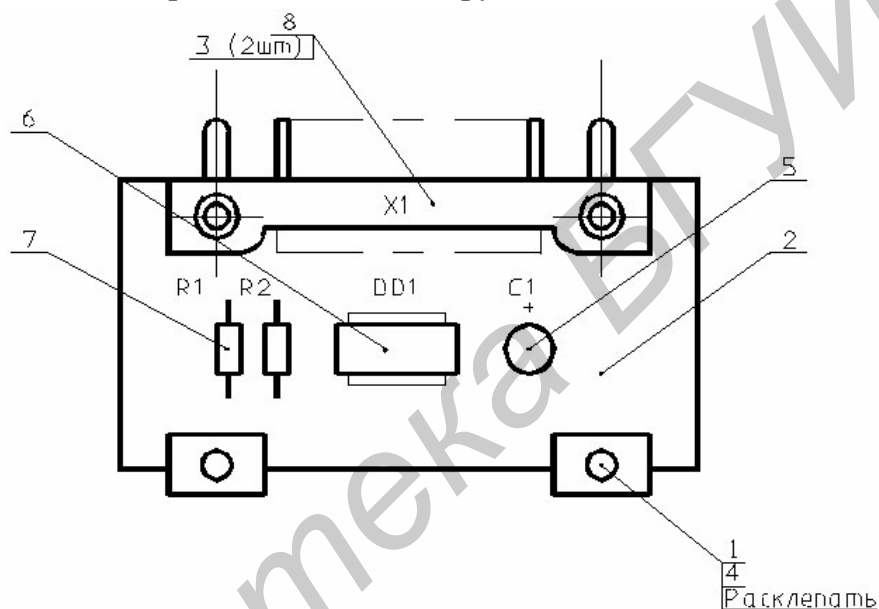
Фрагмент сборочного чертежа платы таймера
